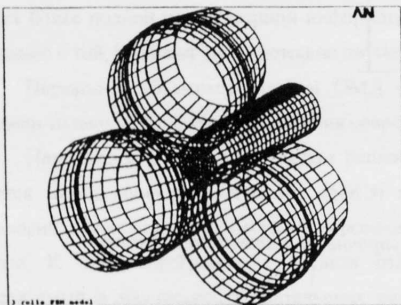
Калибровка рабочего вала стана ПВП 20-60.
